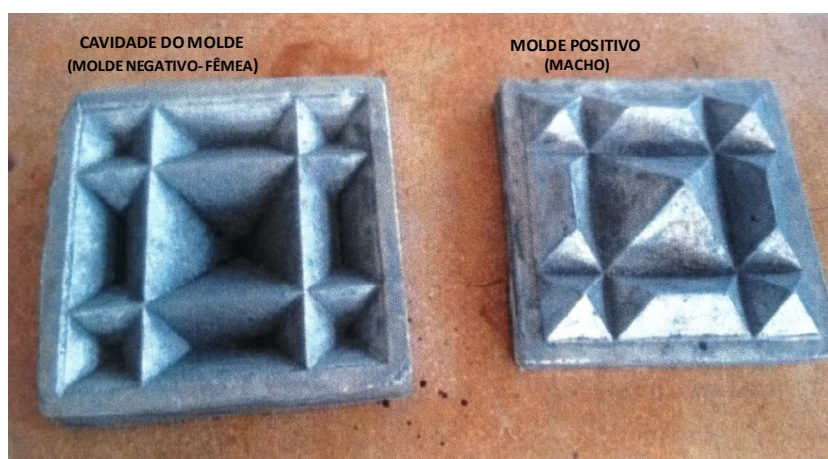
MOLDE DE ALUMÍNIO PARA MOLDAGEM POR COMPRESSÃO
